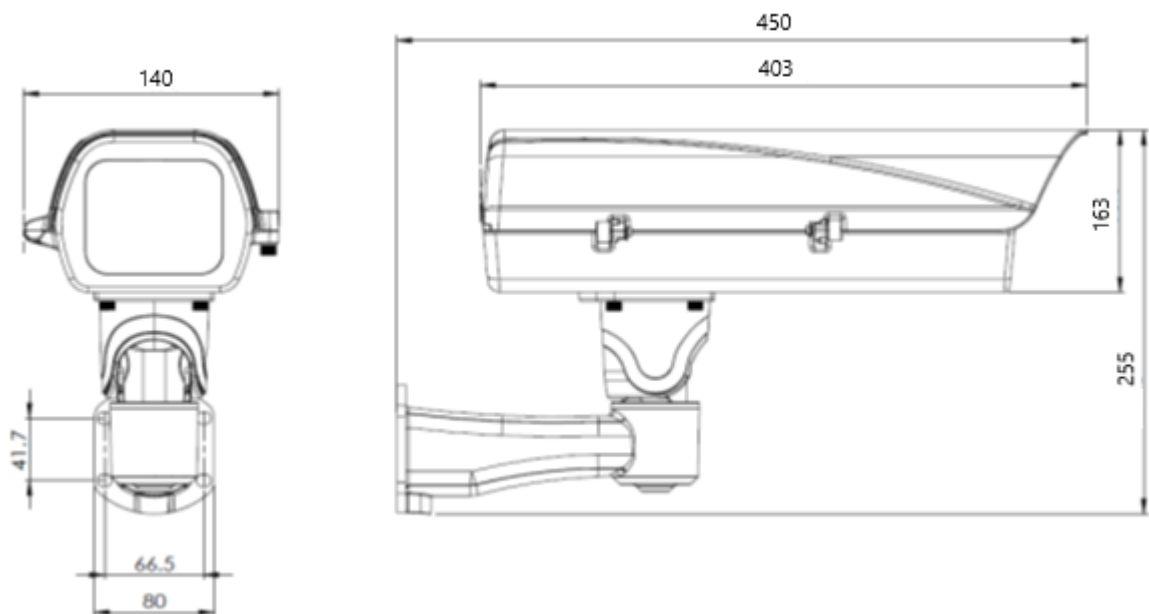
Габаритные размеры IP-видеокамеры SDP-856
